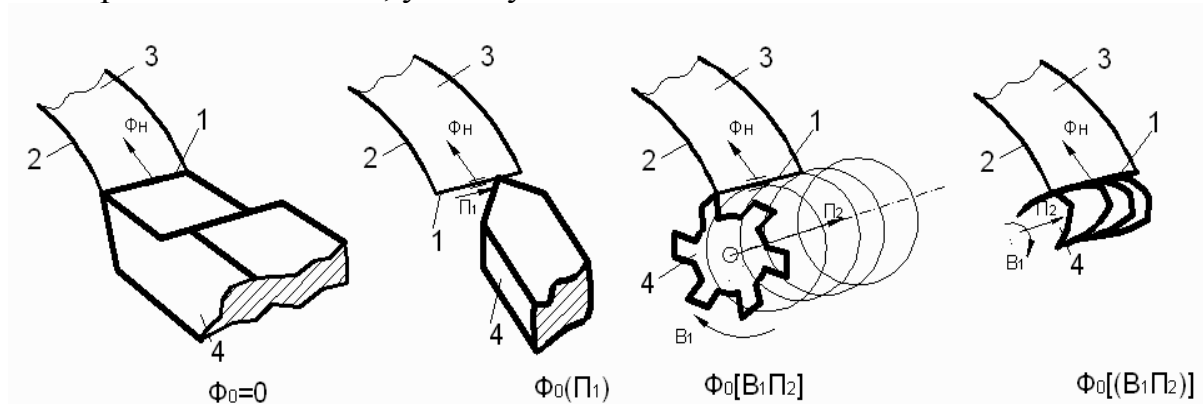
Способы формообразования образующей на поверхности изделия в технологическом механизме: а – копированием; б – подобием; в – касанием; г – обкатом. 1 – образующая; 2 – направляющая; 3 – образуемая поверхность; 4 – режущий инструмент; Φ_0 – движение формообразования образующей 1; Φ_n – движение формообразования направляющей 2
